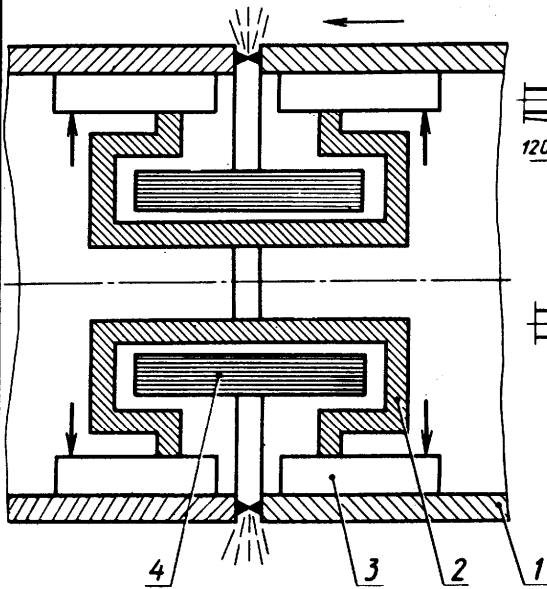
Схема контактной сварки внутритрубной машиной
